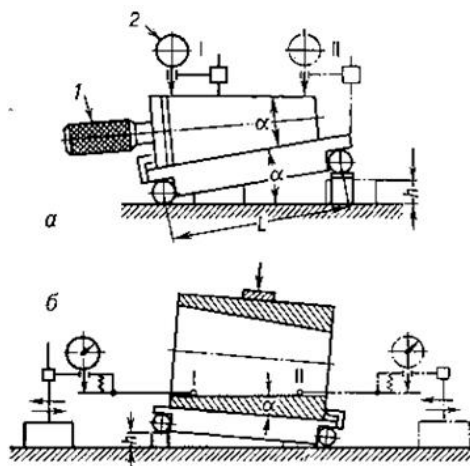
Вимірювання кута при використанні синусної лінійки: а – зовнішнього конуса; б – внутрішнього конуса; 1 – конусний калібр; 2 – відлікова головка; I і II – положення відлікової головки
